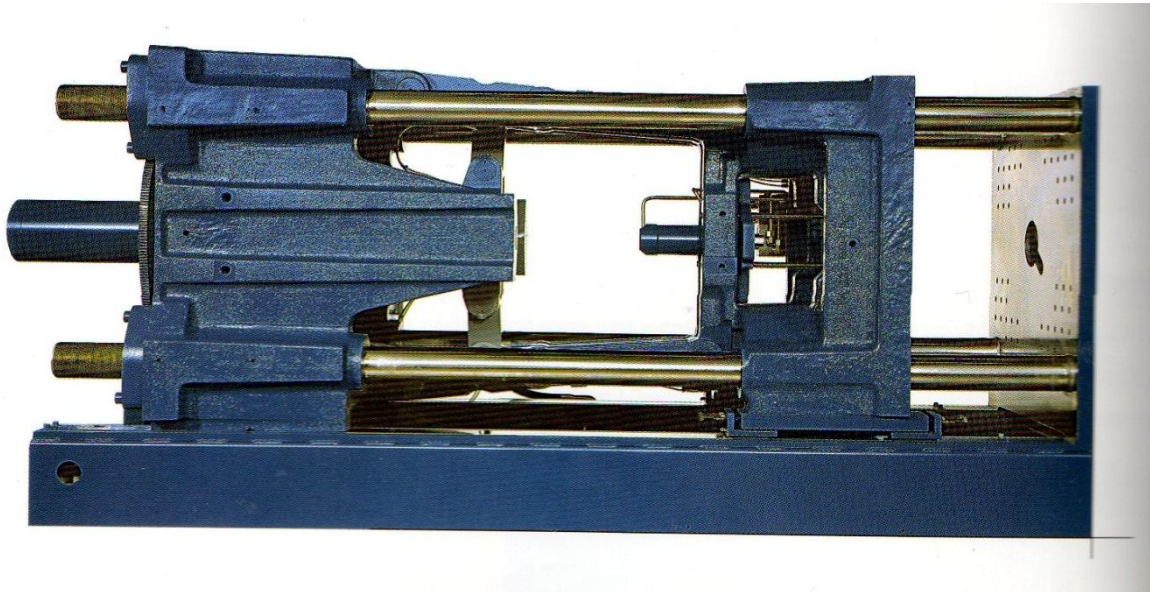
Partes principales de la unidad de cierre antes señalados de una maquina con cierre de pistón.
